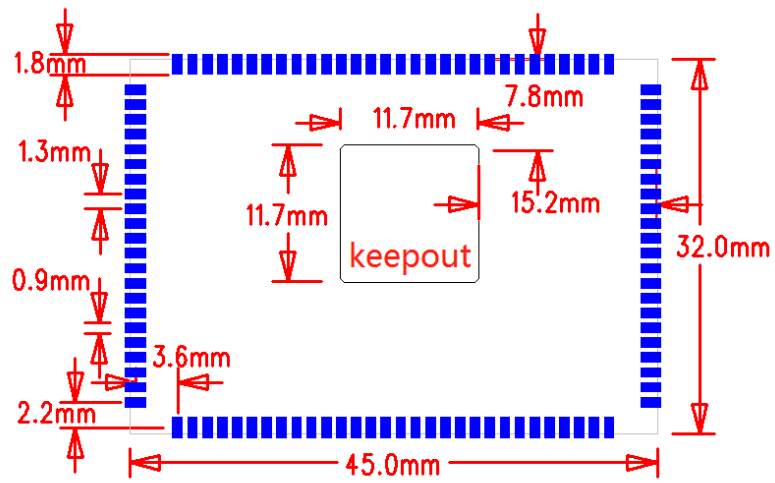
推荐的 PCB 封装焊盘尺寸(单位 mm)
